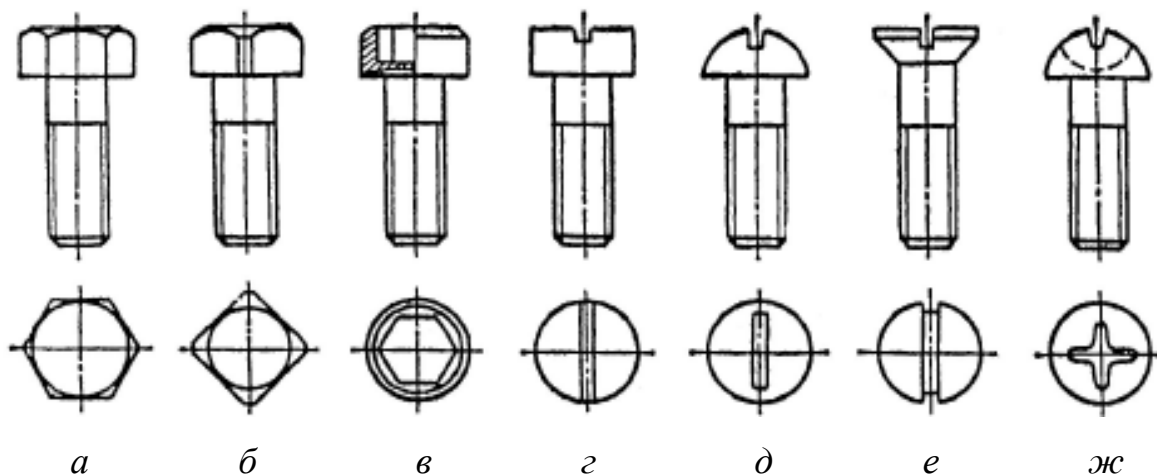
Загальний вид болтів з шестигранними голівками
